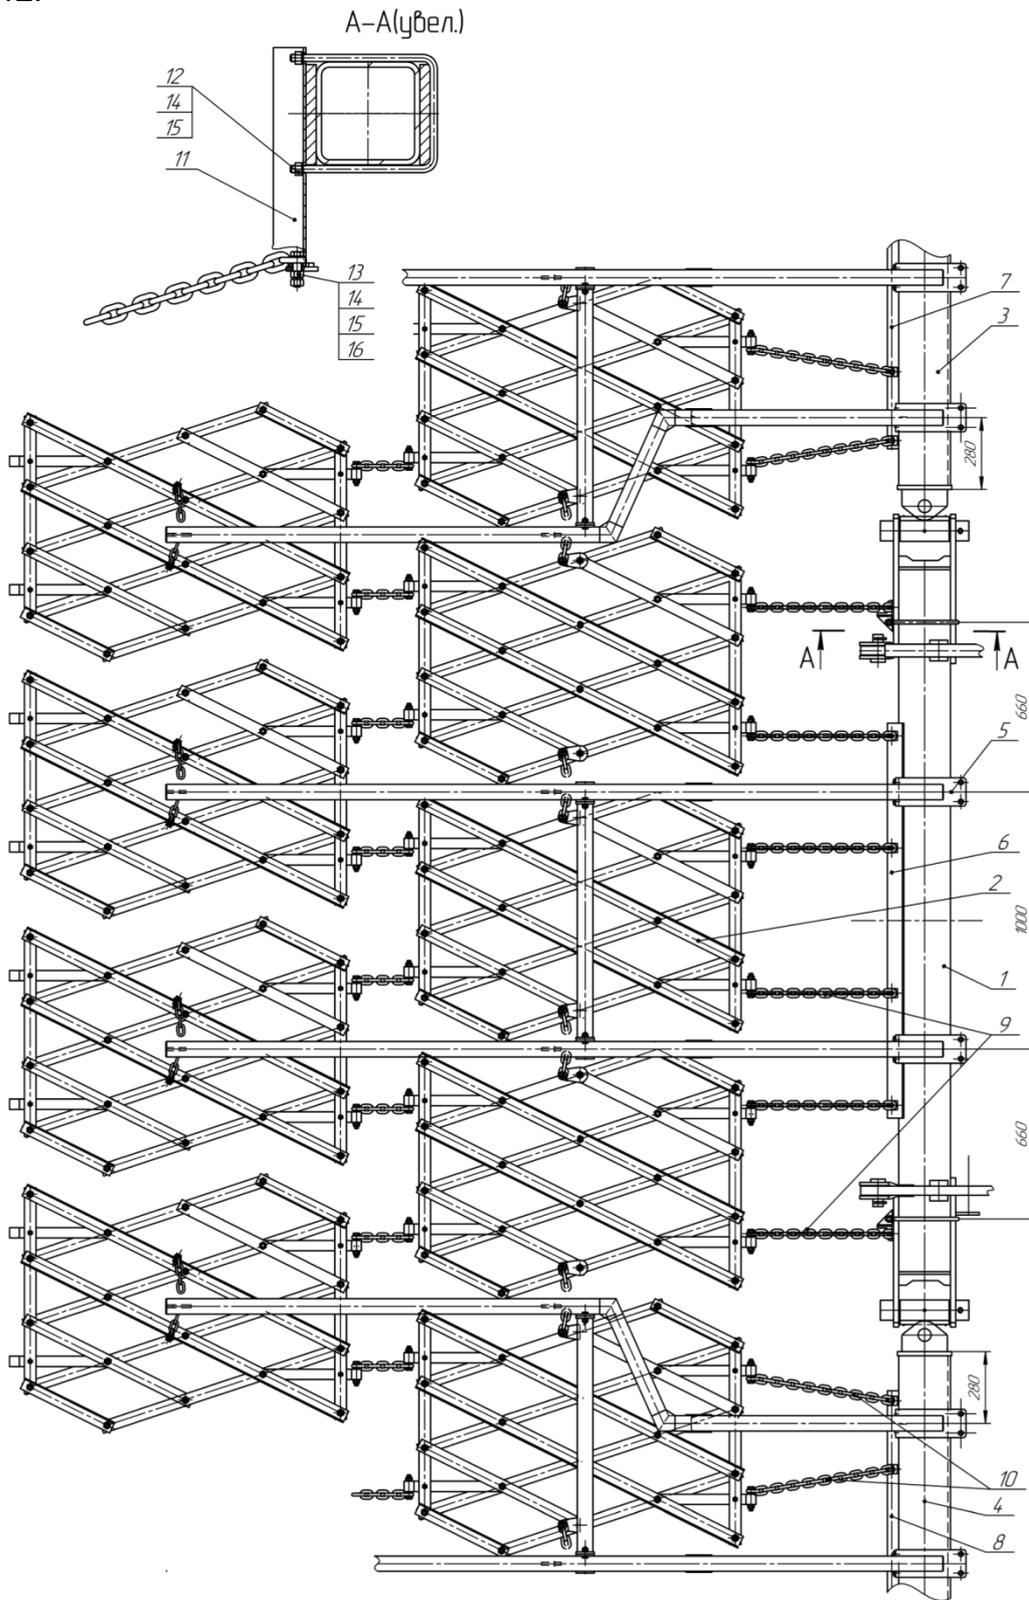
Навешивание борон на брус центральный и боковой. 1 – брус центральный, 2 – борона БЗС-1, 3-брус боковой левой, 4- брус боковой правый, 5– стрела, 6– тяга №2, 7- тяга левая №3, 8- тяга правая №4 ,9и10-
